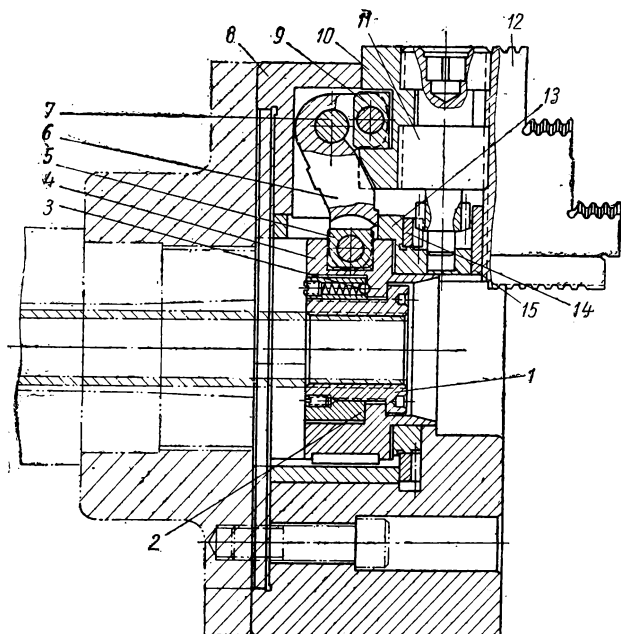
Трехкулачковый клиновой патрон, позволяющий обрабатывать прутковый материал.
